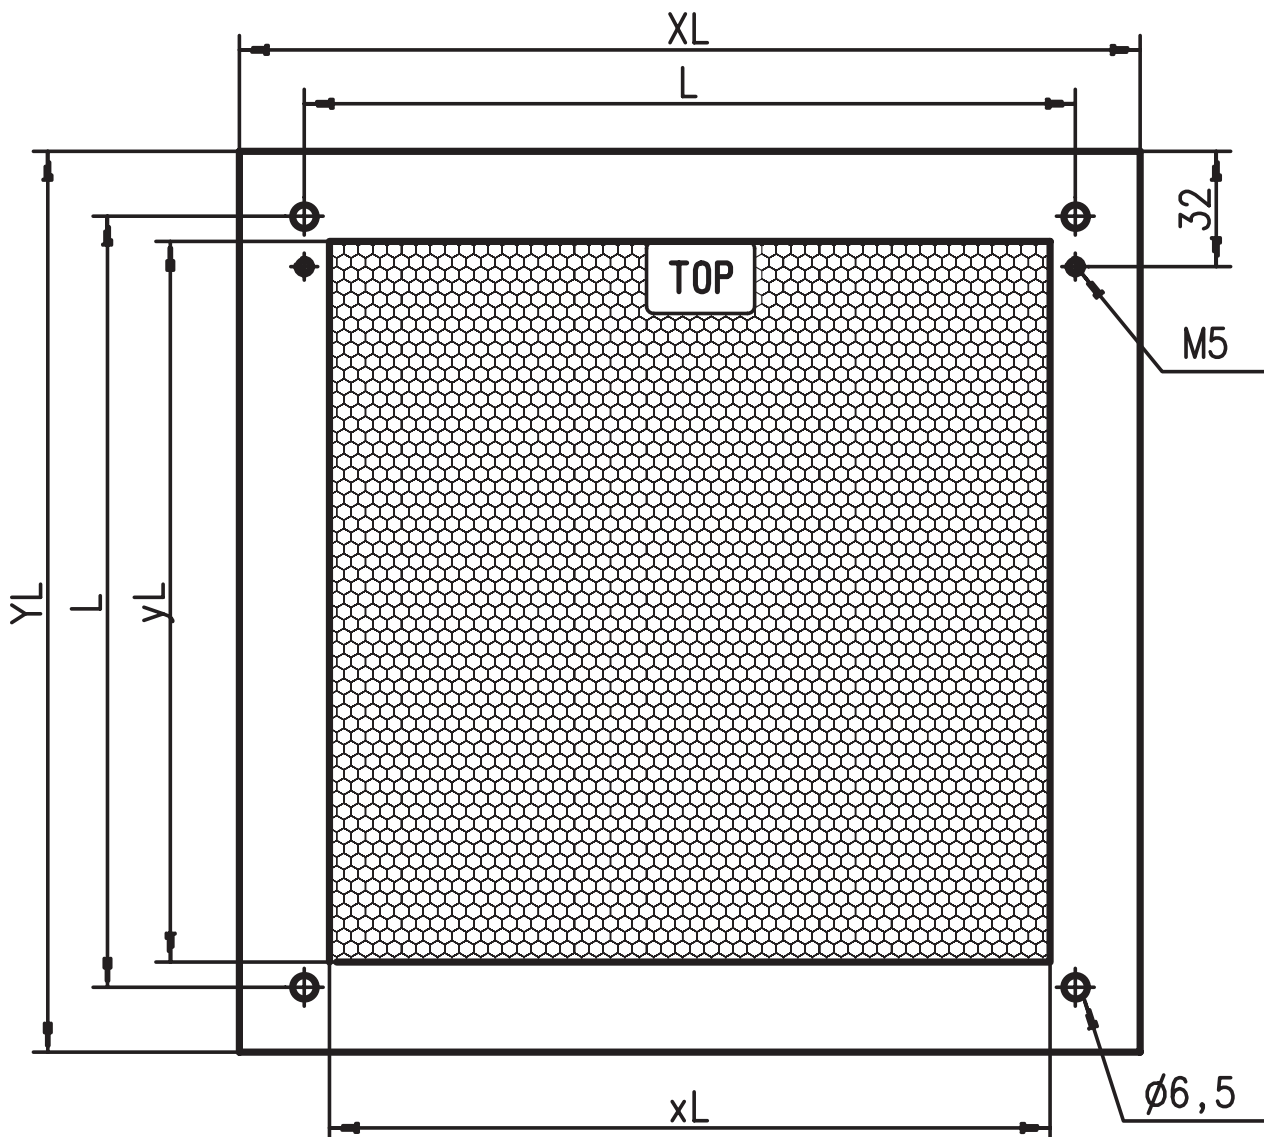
Dibujo acotado de una cinta reflectora sobre una placa de soporte
